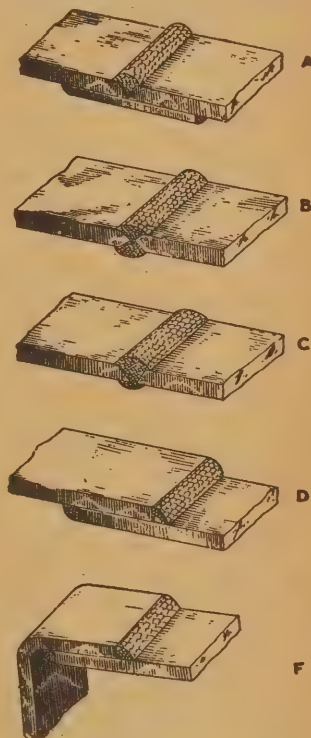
bis 12. Formgebungen für die Ausführung von Lichtbogenschweißungen.
